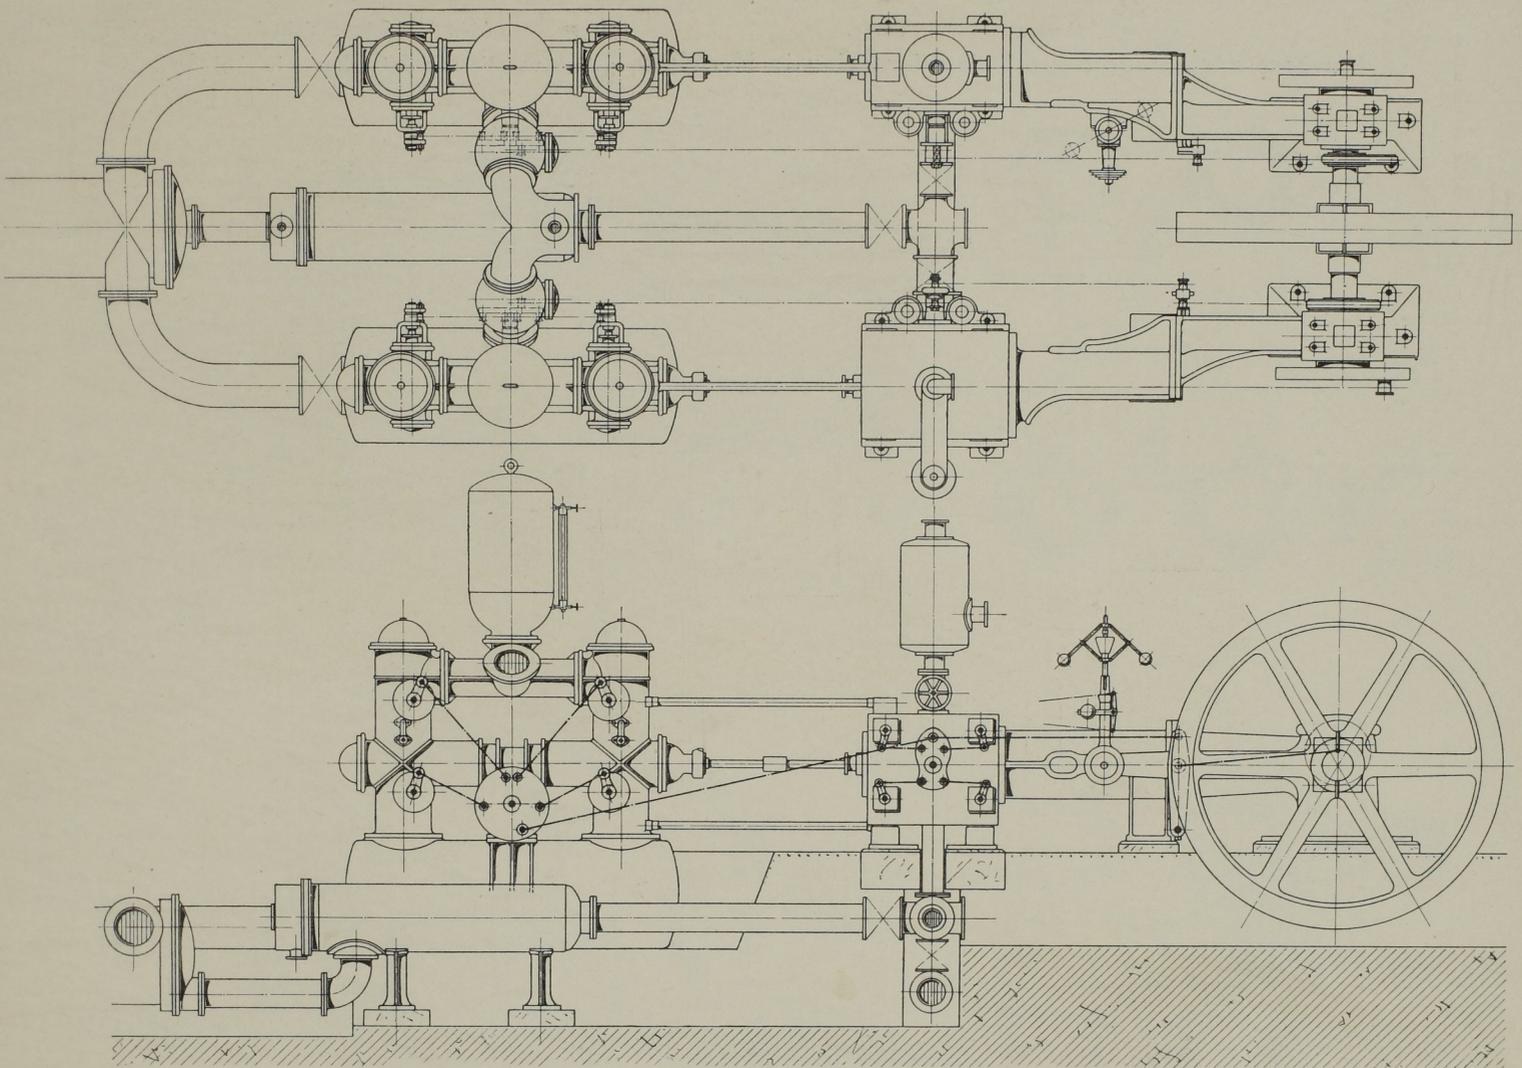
Grundriss und Seitenansicht der Pumpmaschine. Massst. 1:64.
